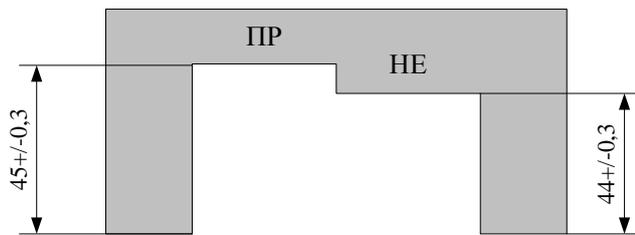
Калибр для проверки глубины вытяжки штампа
